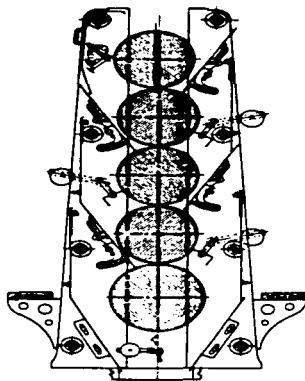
Sección transversal de una trituradora, provista de cinco rodillos superpuestos (cortesía de French Oil Mill Machinery, Co.)
